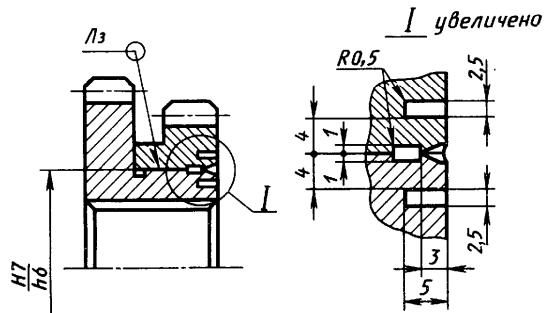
Соединение блока зубчатых колес лазерной сваркой
